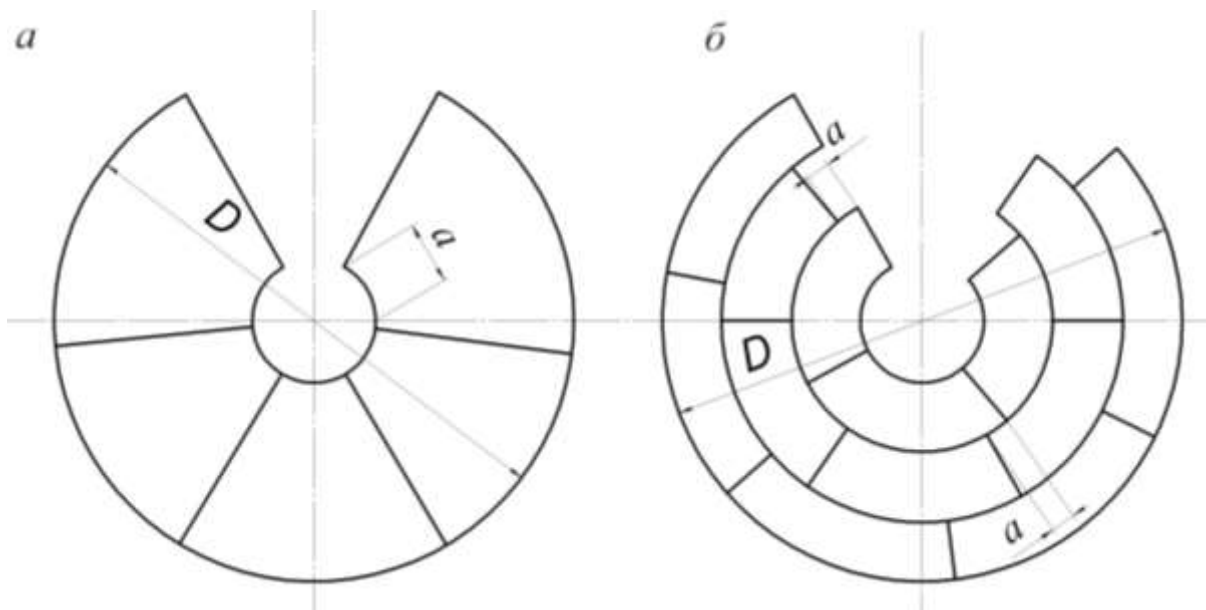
Розташування зварних стиків у плоских заготовках-розгортках конічних днищ, виготовлених з окремих частин:
